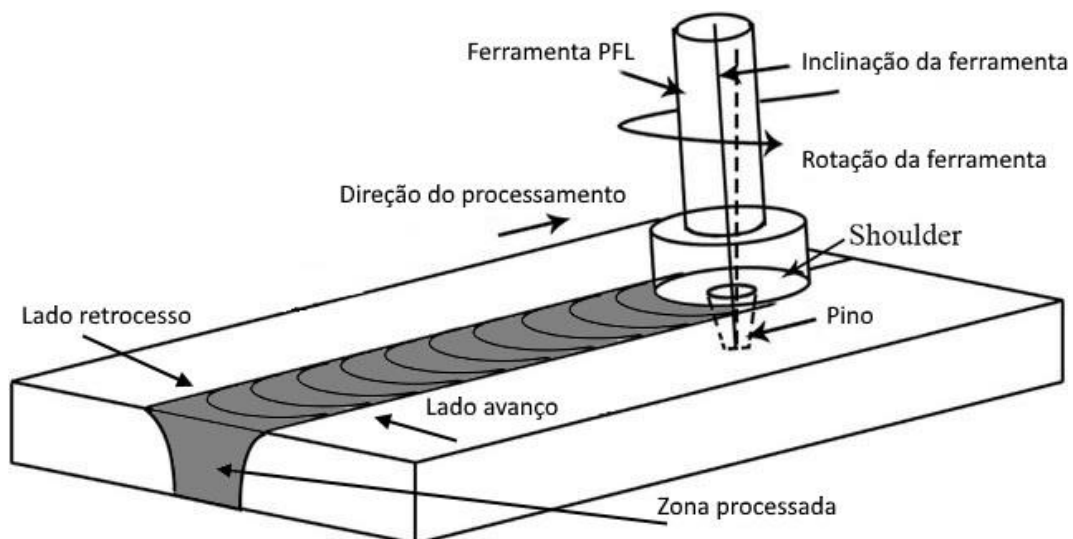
Esquema da realização da soldadura por fricção linear – adaptado de [18]
